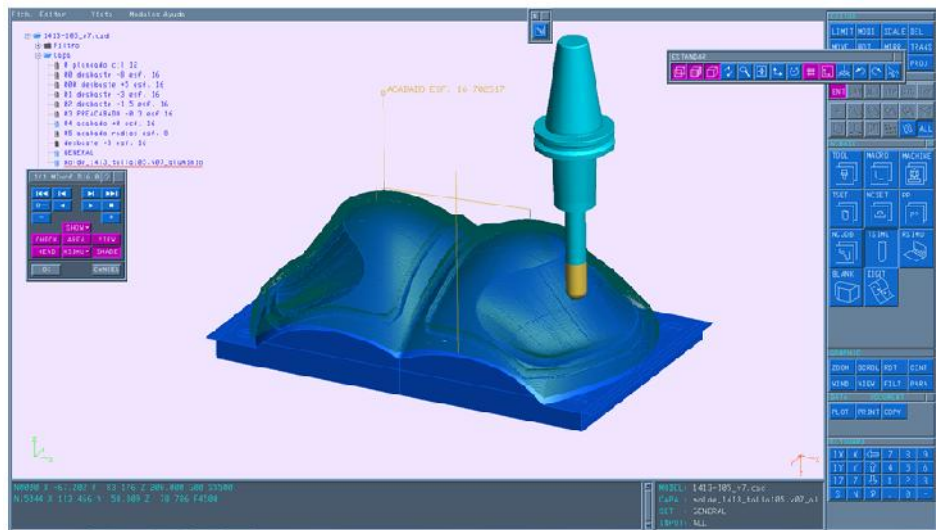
Mecanizado del molde macho por ordenador
